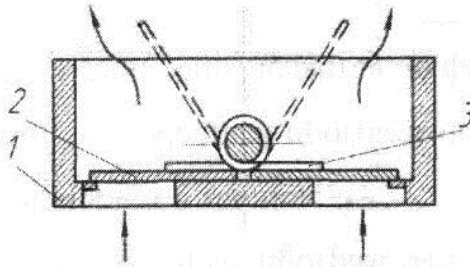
Зворотний клапан типу «метелик»: 1 – корпус-сідло; 2 – пластини; 3 – пружина
